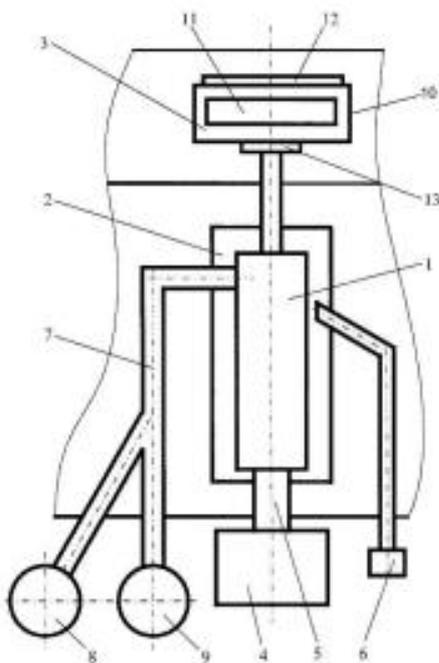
Газоперекачивающий агрегат компрессорной установки из патента RU 2 200 255 С1
